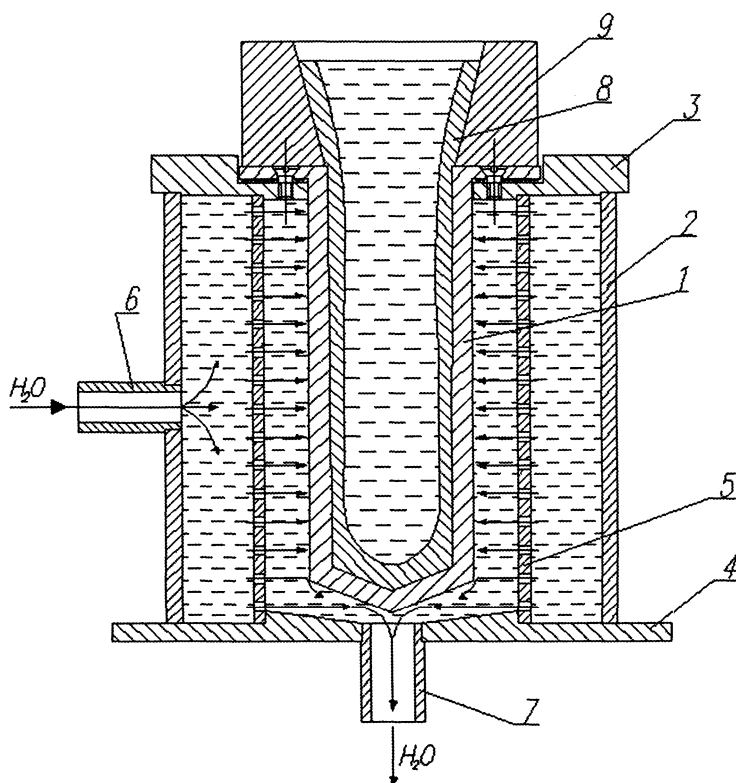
Схема литья в кокиль со струйной системой охлаждения: 1 – стакан; 2 – корпус; 3 – верхний фланец; 4 – нижний фланец; 5 – экран; 6 – подводящий патрубок; 7 – отводящий патрубок; 8 – отливка; 9 – захват
